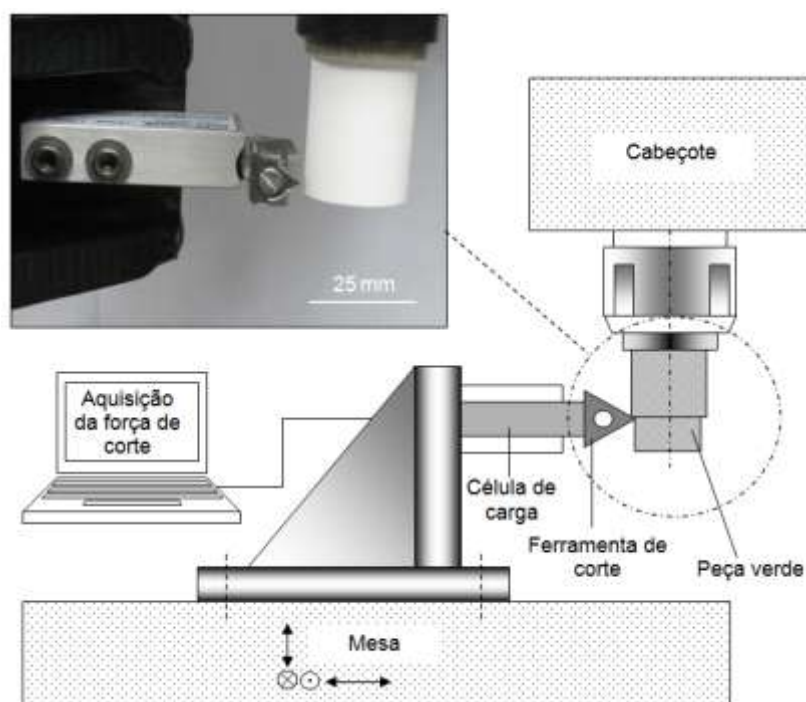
Montagem esquemática do banco de ensaio de usinagem
